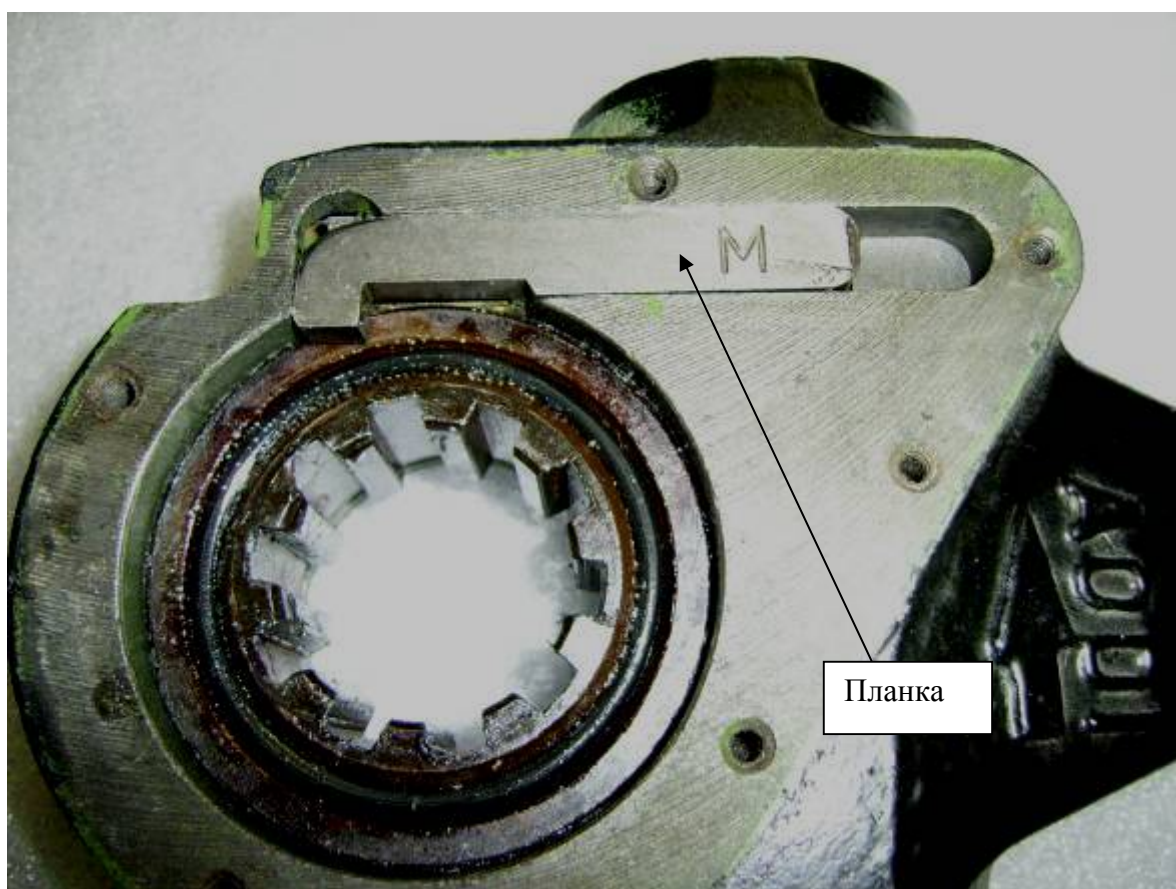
Положение фигурной планки храпового механизма в корпусе
